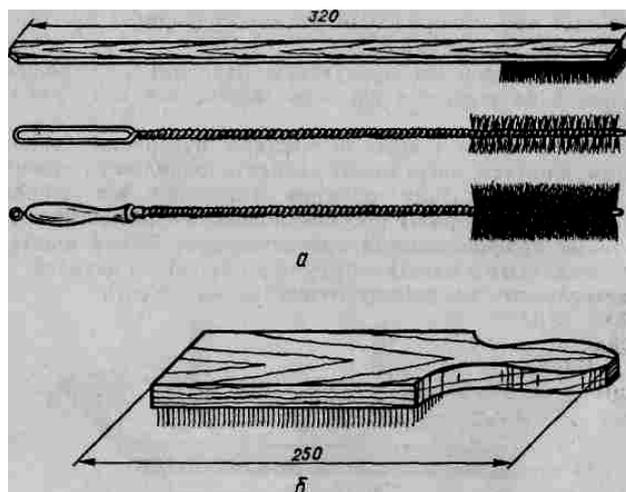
Інструменти для очищення металевих поверхнь:
